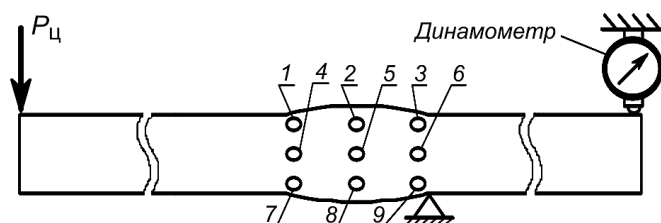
Схема нагружения образца. (1–9 – области измерения твердости в сварном шве.)
